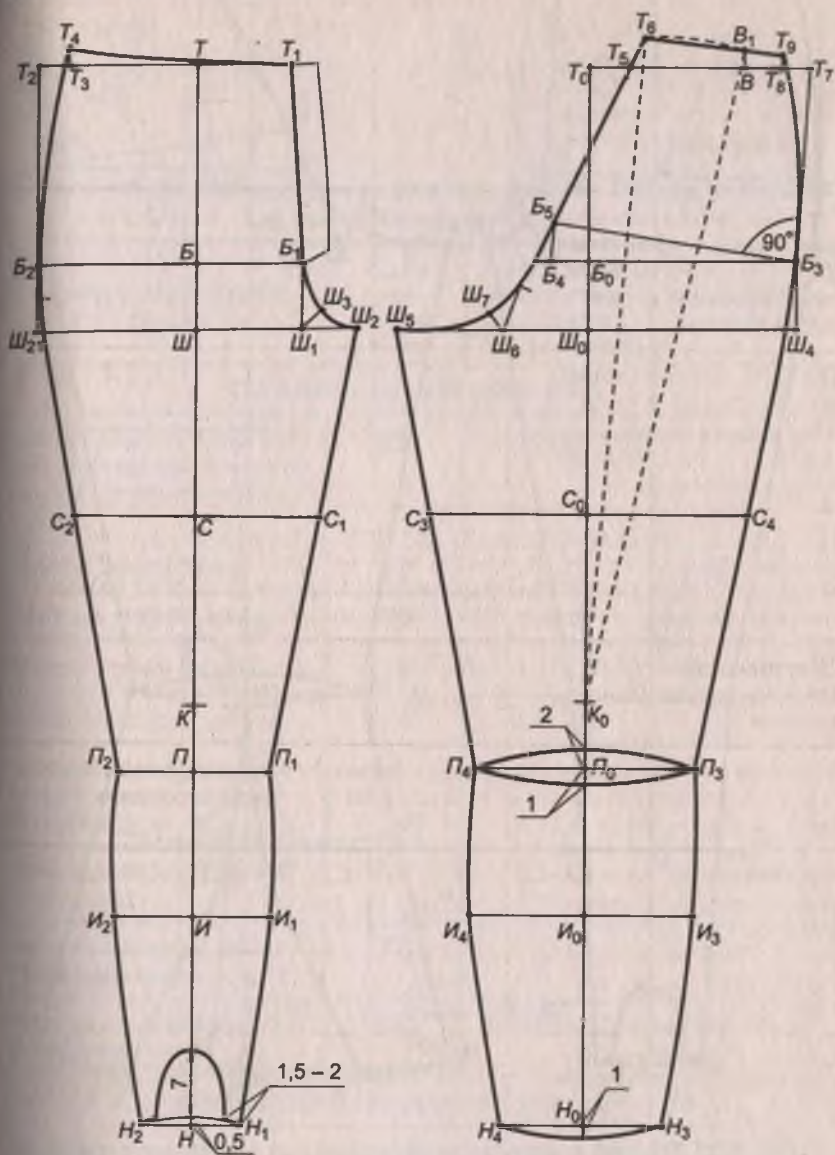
Чертеж конструкции брюк бриджи на базовой основе брюк джинсы
